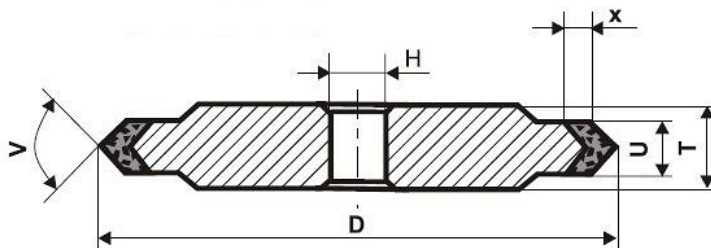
Конусний алмазний круг на металевій зв'язці
